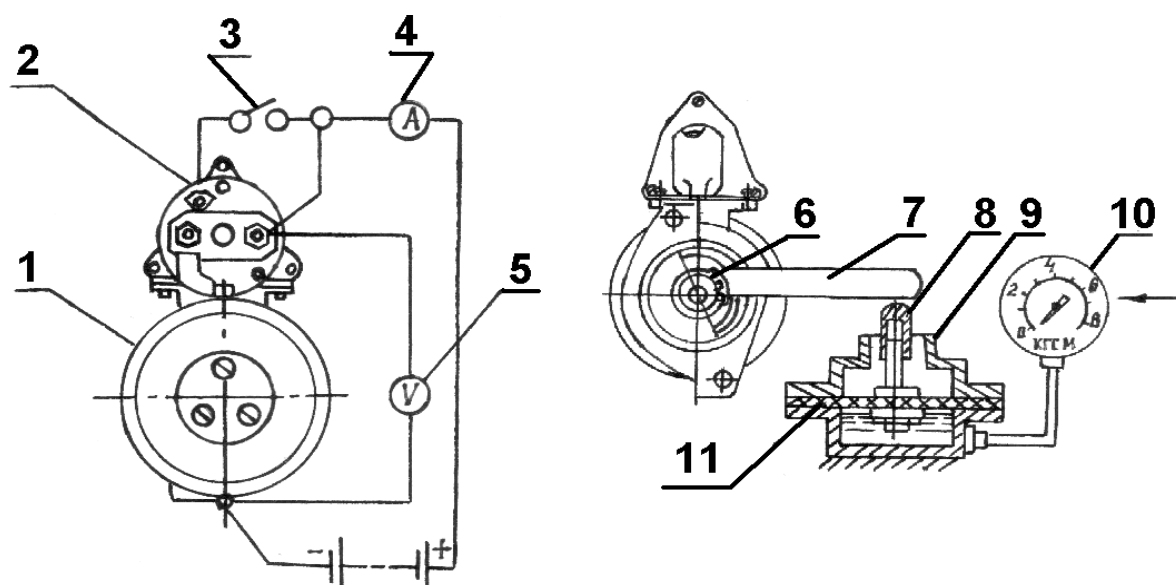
Схема включения и устройство приборов для испытания стартеров:
